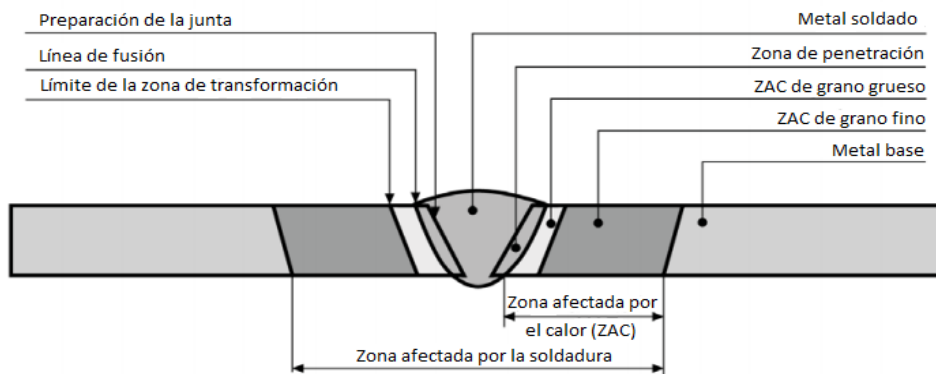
Zonas afectadas por la soldadura (15).
